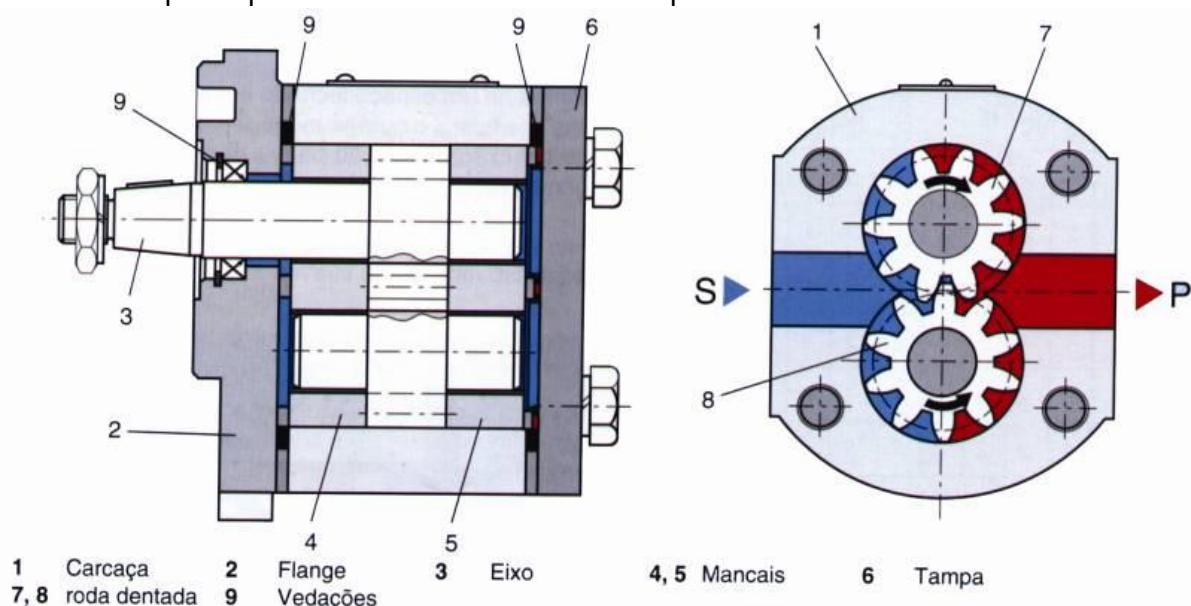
Partes de uma bomba de engrenagem externa.
